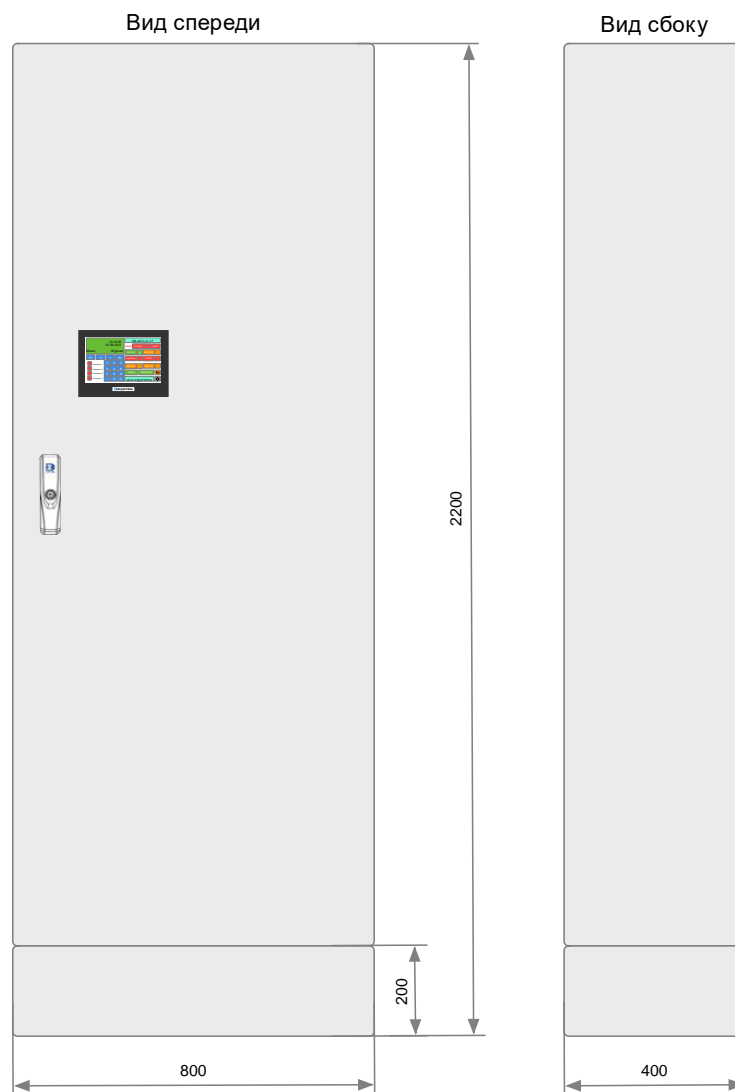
Внешний вид и габаритные размеры концентратора с одностворчатой дверью
